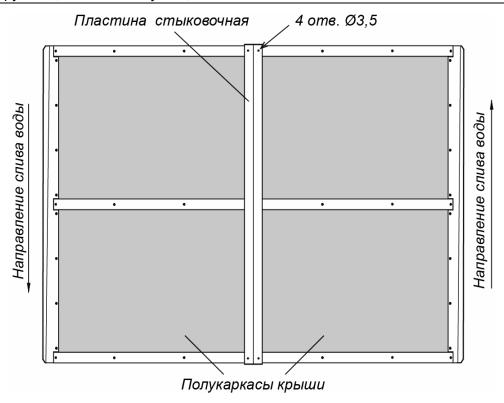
Вид сверху соединенных полукаркасов (1) и (2) с установленной стыковочной пластиной (6)
